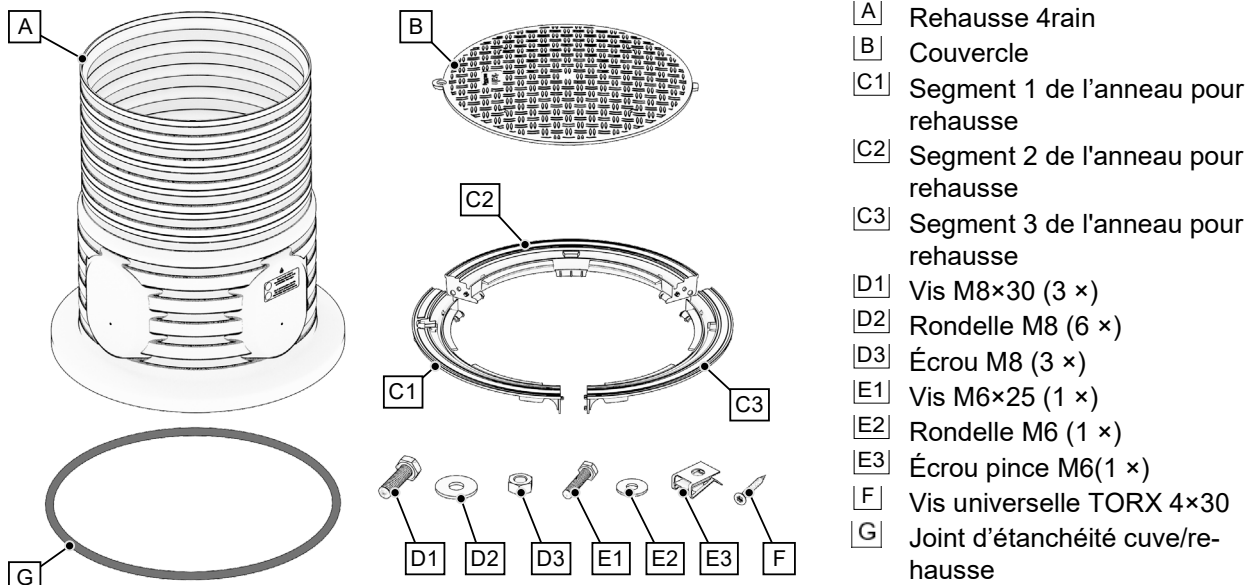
Rehausse 4rain et couvercle – Vue éclatée
